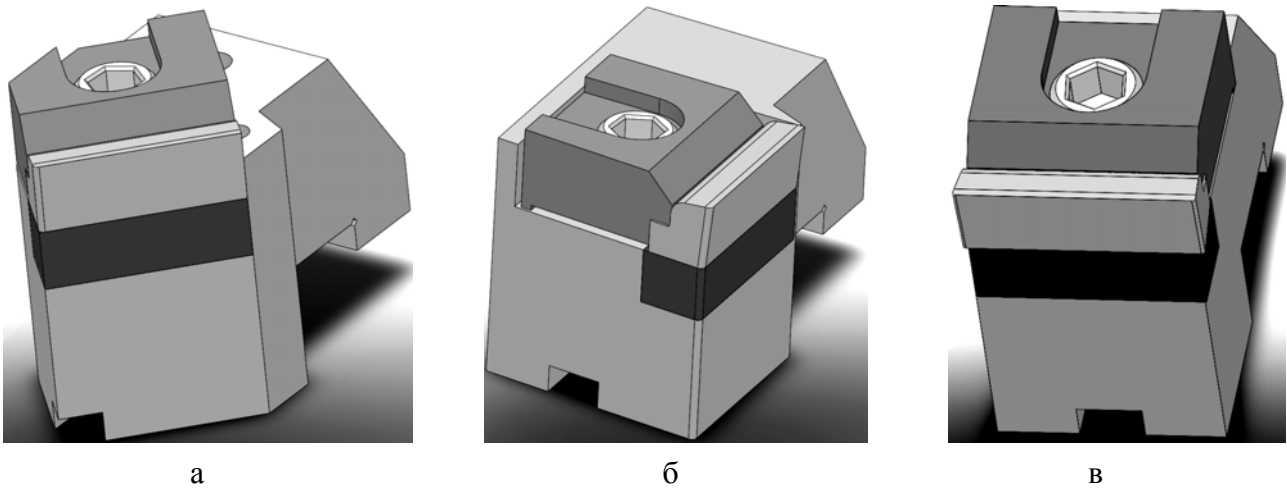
Система блоков-вставок для тяжелого токарного станка:
